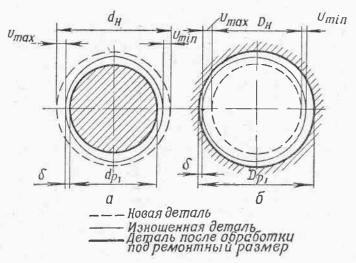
Определение нормализованных ремонтных размеров: а — для вала; б — для отверстий
